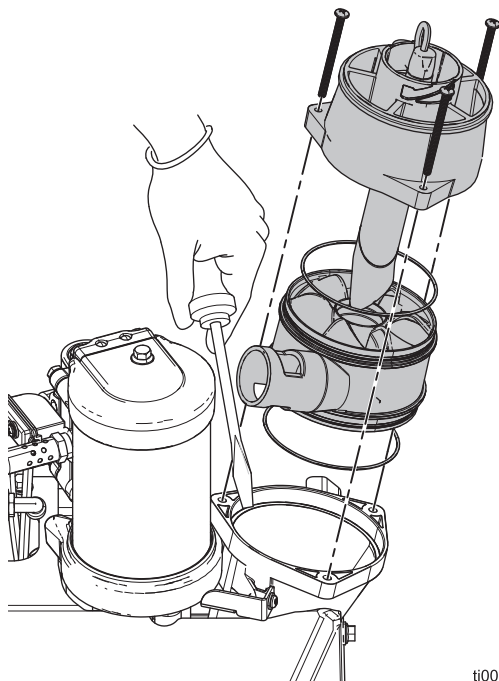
Conjunto da tampa do funil e do filtro do funil
